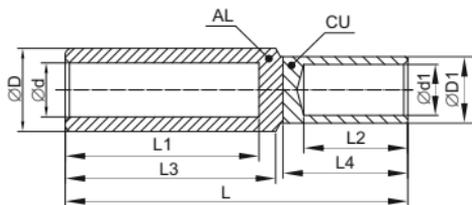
Гильзы медноалюминиевые, внешний вид и габаритные размеры.
